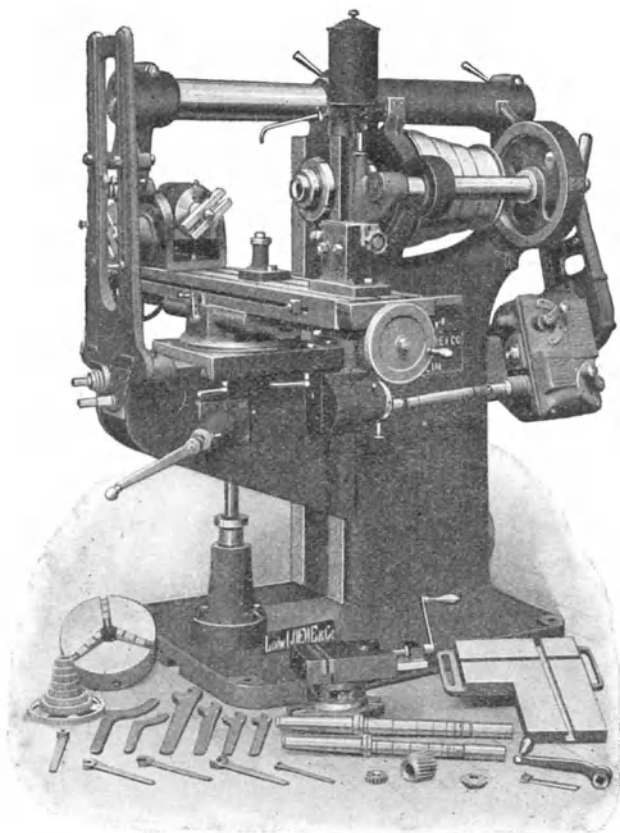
Die Universalfräsmaschine von L. Löwe & Co.
